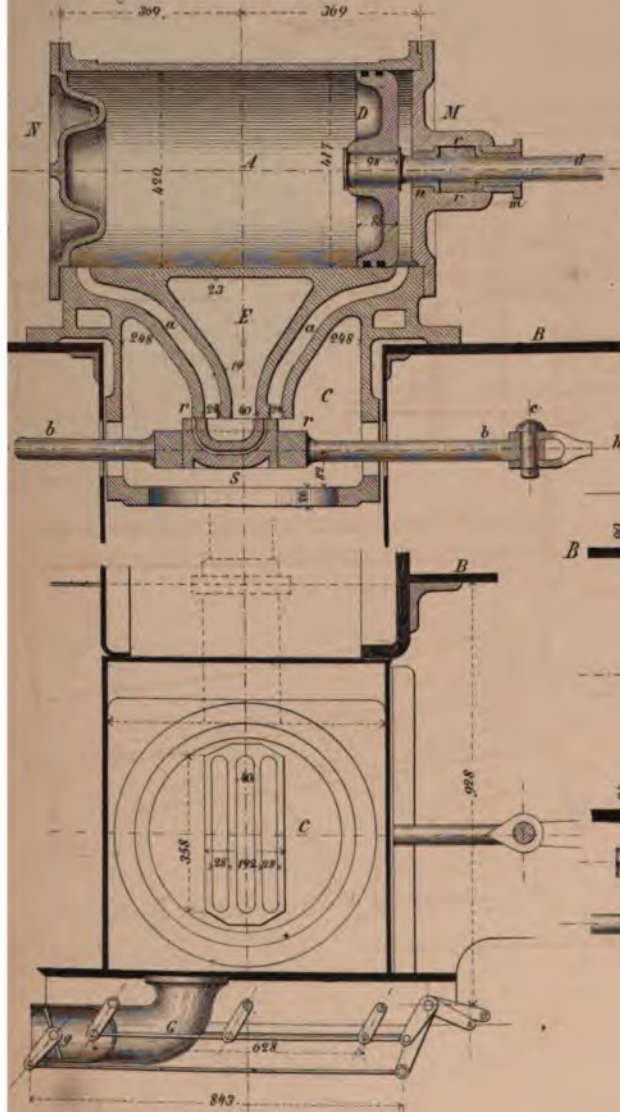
Ansicht der Planflächen im Schieberkasten.
